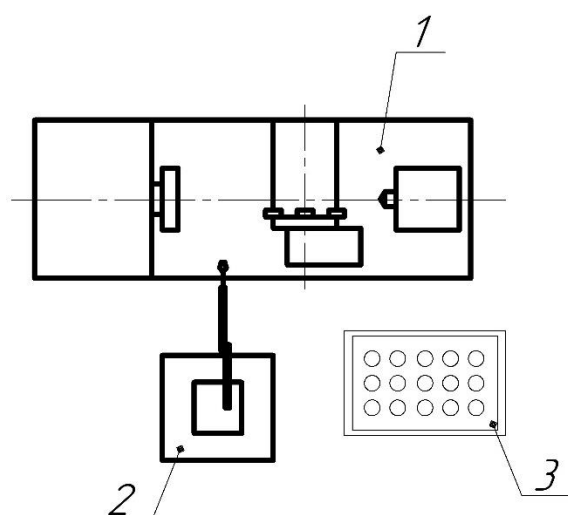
Схема автоматизированного модуля токарного станка с ЧПУ
